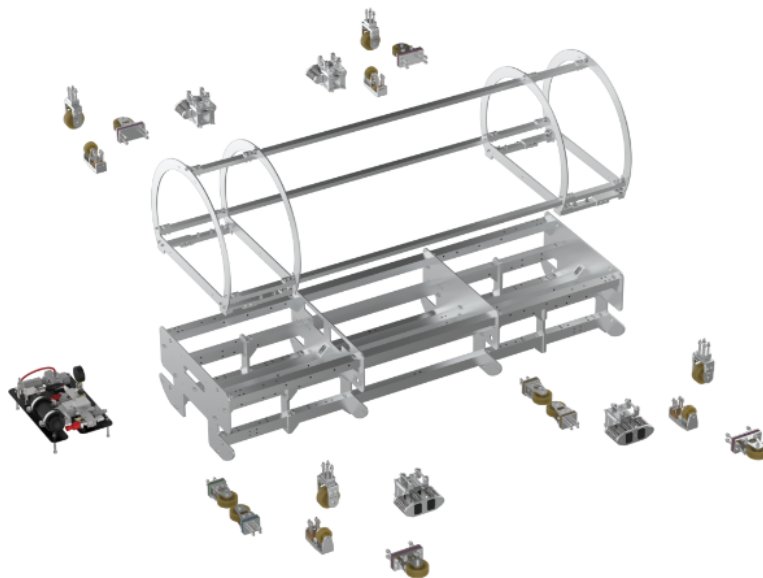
Vista isométrica de los componentes mecánicos de Kénos
